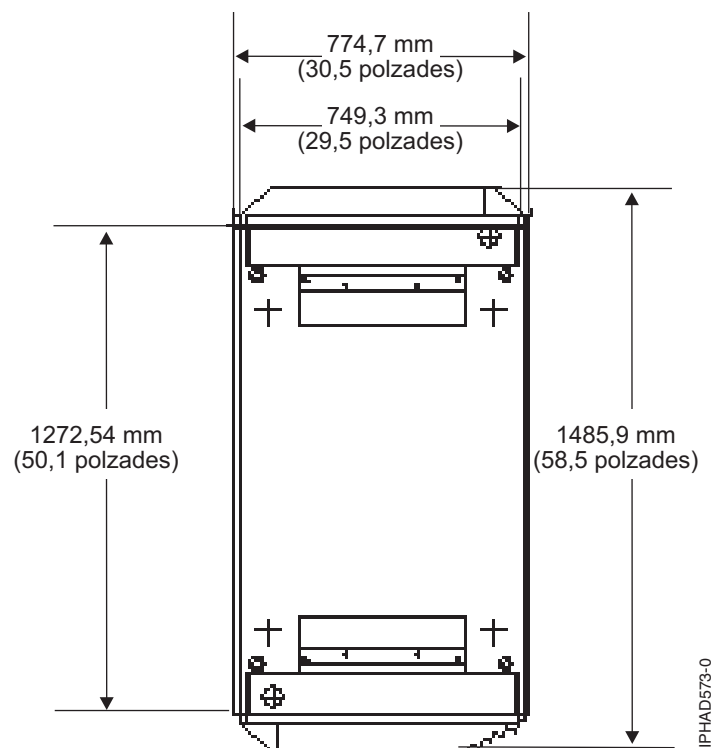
Vista de planta per a sistemes d'un sol bastidor amb portes extraplans
